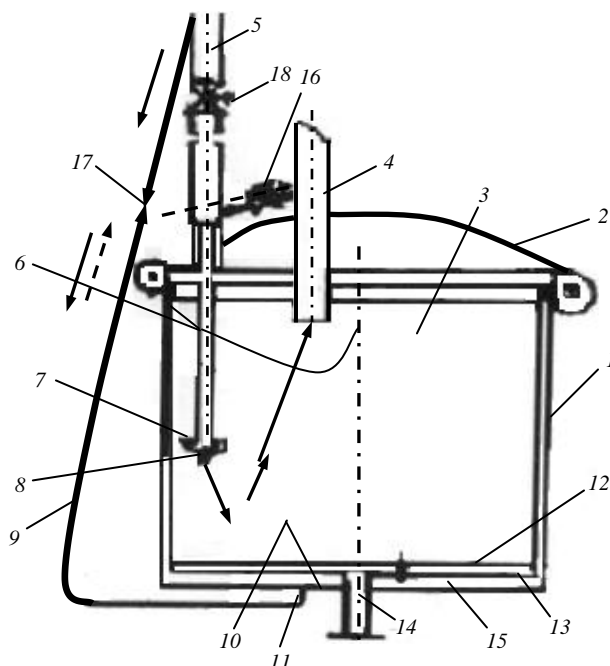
Схема камерного питателя пневмотранспортной установки
